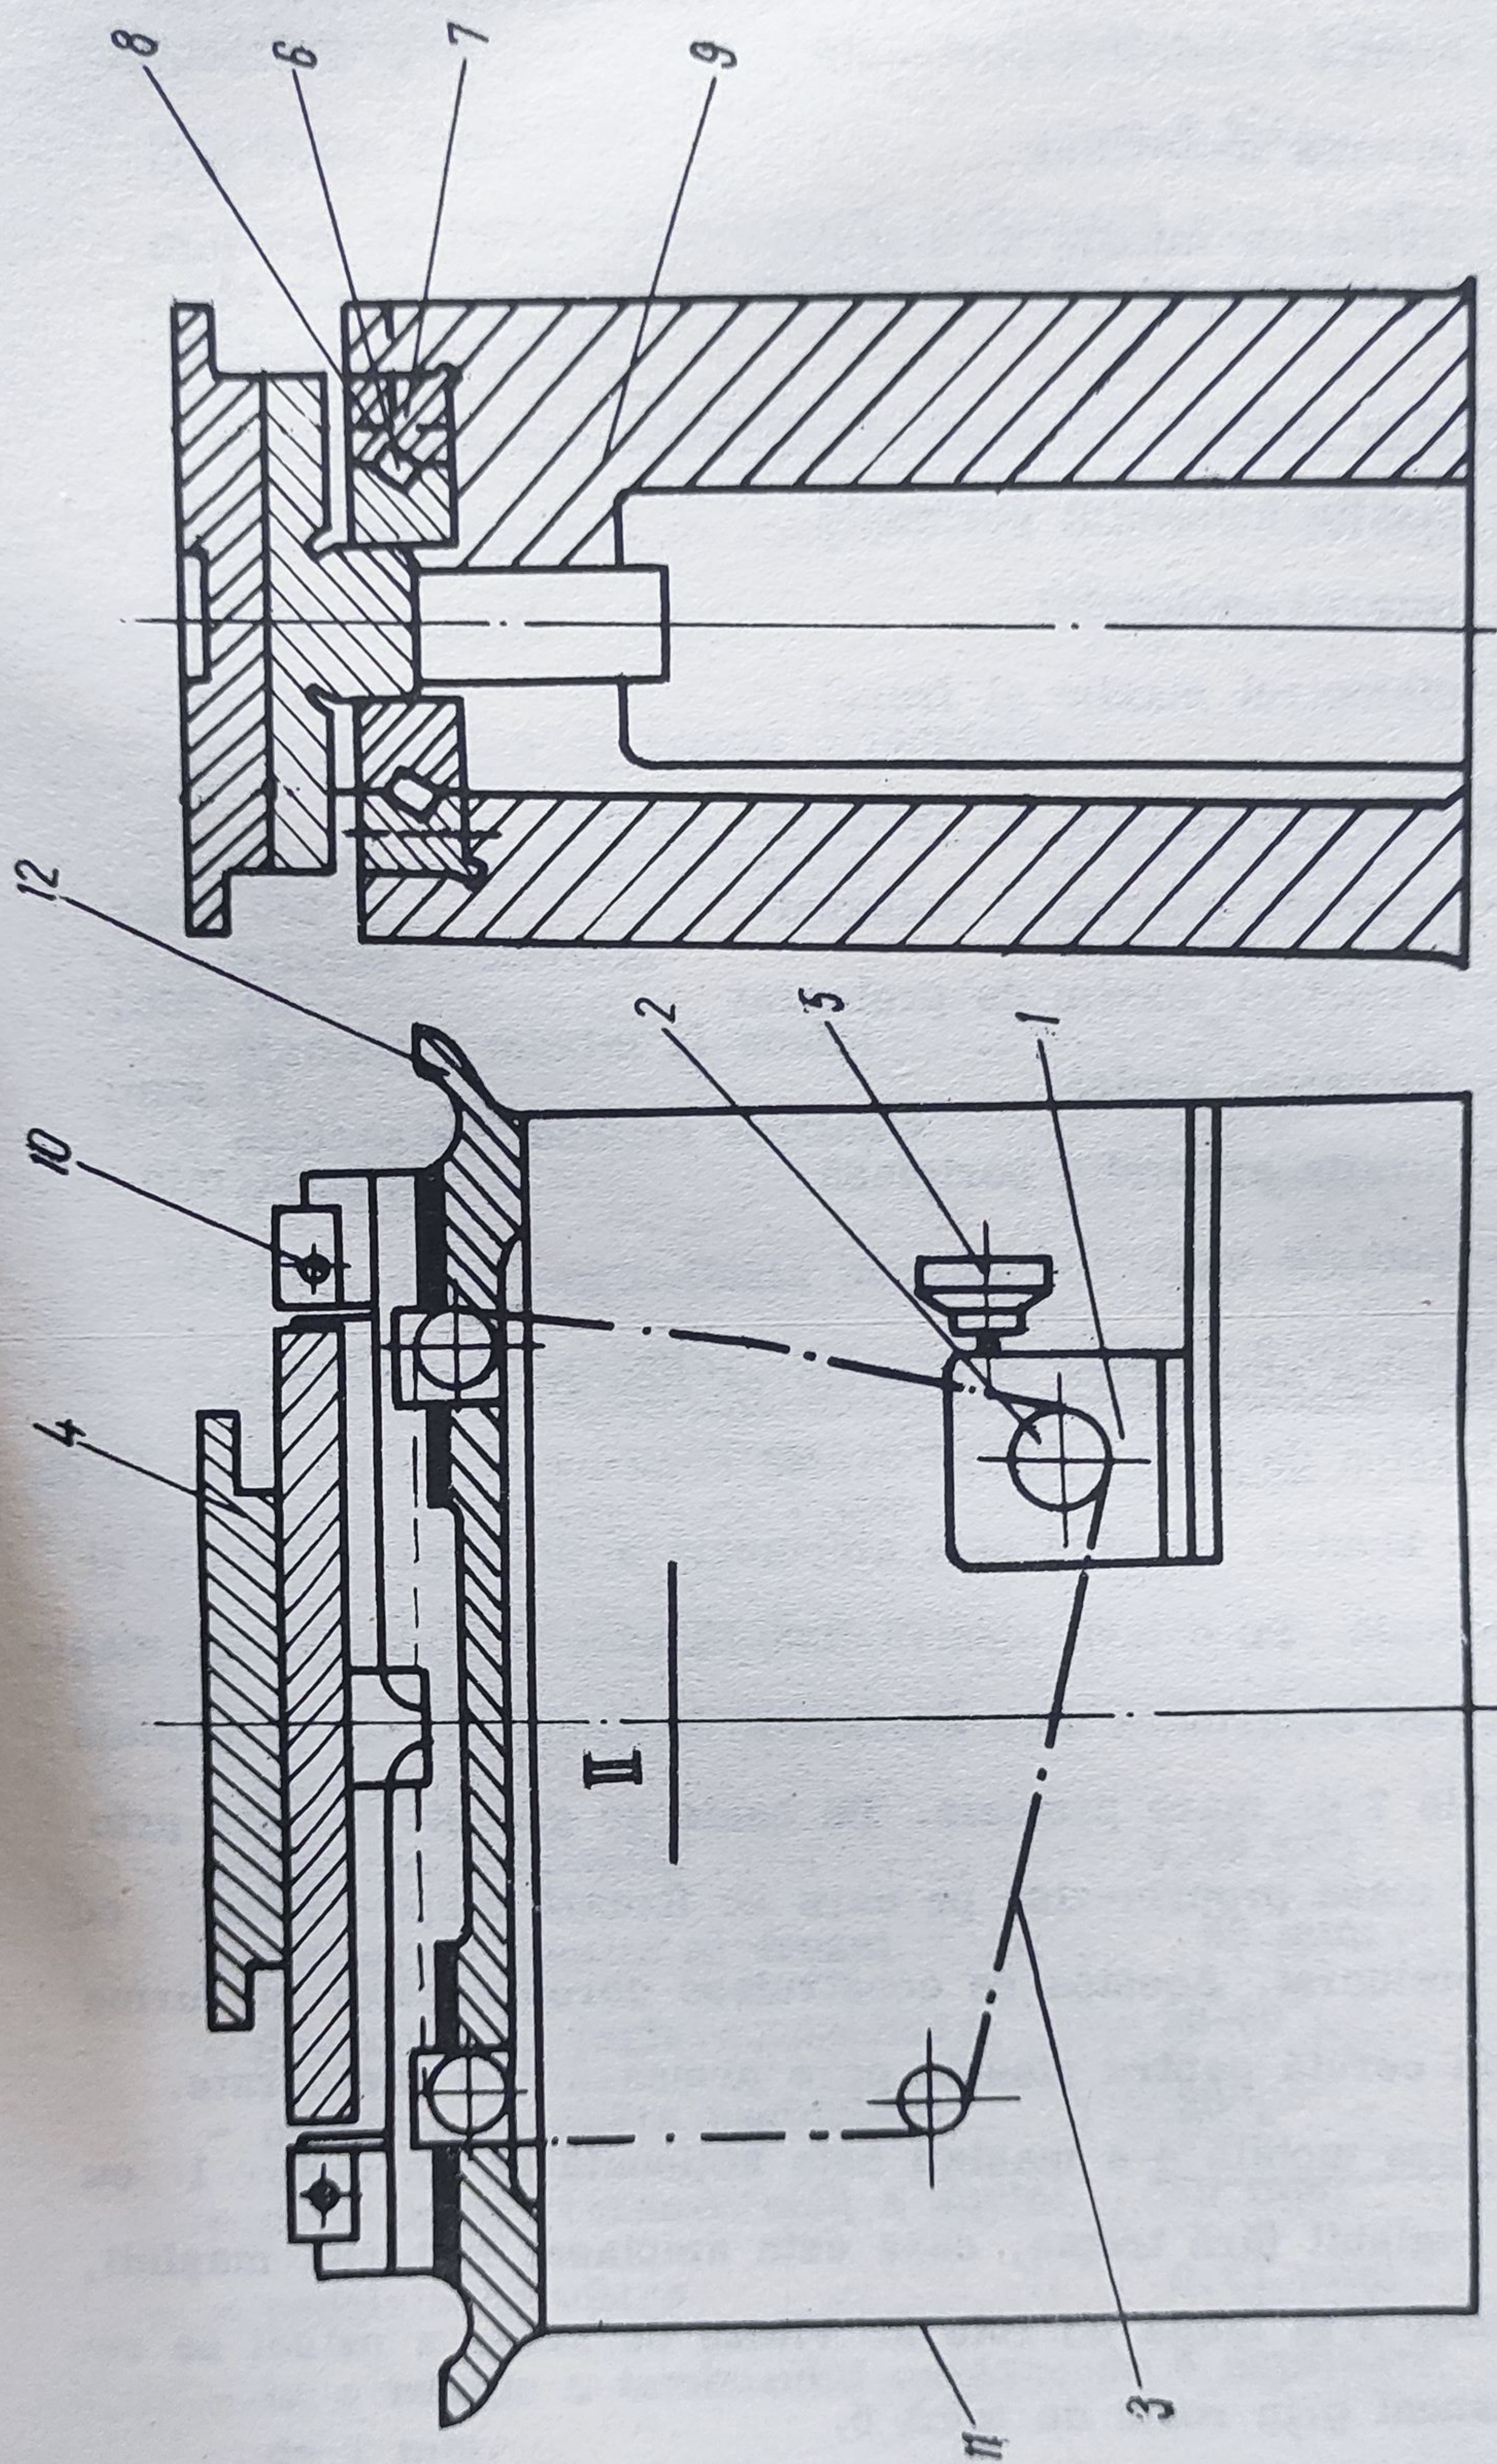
Secțiuni prin mașina de bază a mașinii de frezat universală.
